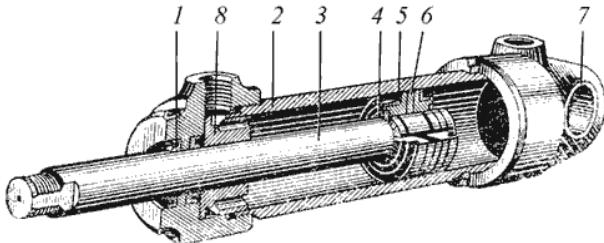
Гидроцилиндр: 1 – грязесъемник; 2 – гильза; 3 – шток; 4 – стопорное кольцо; 5 – манжета; 6 – поршень; 7 – проушина; 8 – грундбукса
